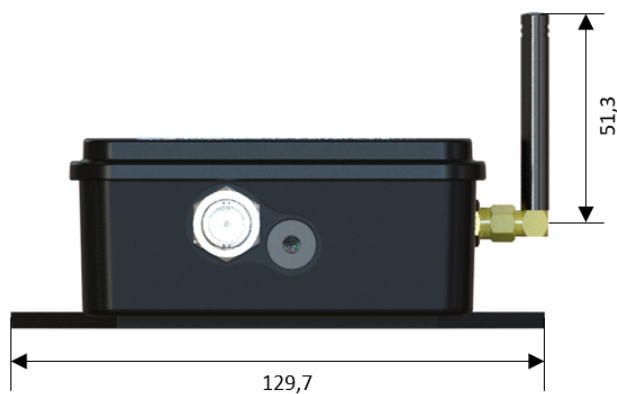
Dimensões [mm] externas do WEGscan400 com presilha para superfícies planas - Vista frontal
